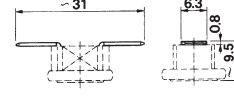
Flachstecker 6.3 x 0.8 seitlich abgewinkelt
